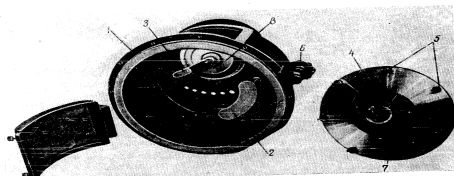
Вращающийся искровой разрядник в разобранном виде: 1 — корпус искрового разрядника; 2 — токосъемник; 3 — неподвижный электрод; 4 — вращающийся диск; 5 — подвижный электрод (7 шт.); 6 — щетка для регулирования тока искры; 7 — текстолитовая втулка; 8 — фарфоровый проходной изолятор.
